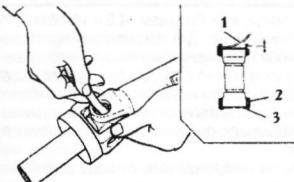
используйте толщиномер для измерения зазора между прижимным кольцом и подшипником (конечный люфт шейки U-образного шарнира)
